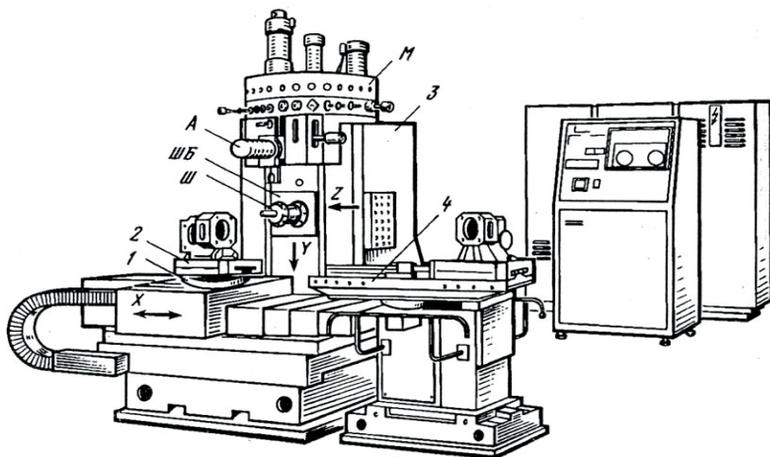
Многооперационный станок фрезерно-сверлильно-расточной группы, оснащённый поворотным столом и двухпозиционным столом-спутником: 1 – стол поворотный; 2 – стол-спутник с заготовкой; Ш – шпиндельный узел; ШБ – шпиндельная бабка; А – манипулятор; М – магазин инструментальный; 3 – стойка; 4 – загрузочно-разгрузочное устройство
